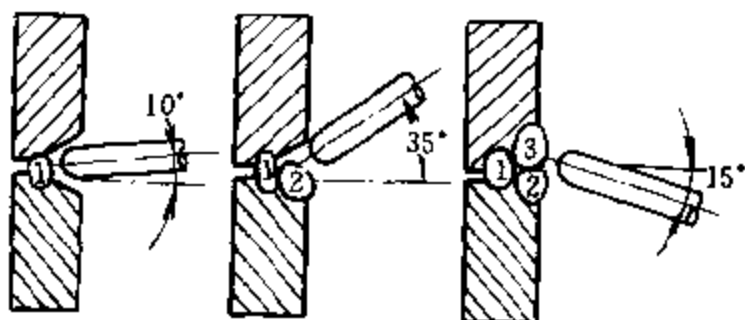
开坡口多层多道焊的焊条倾角
